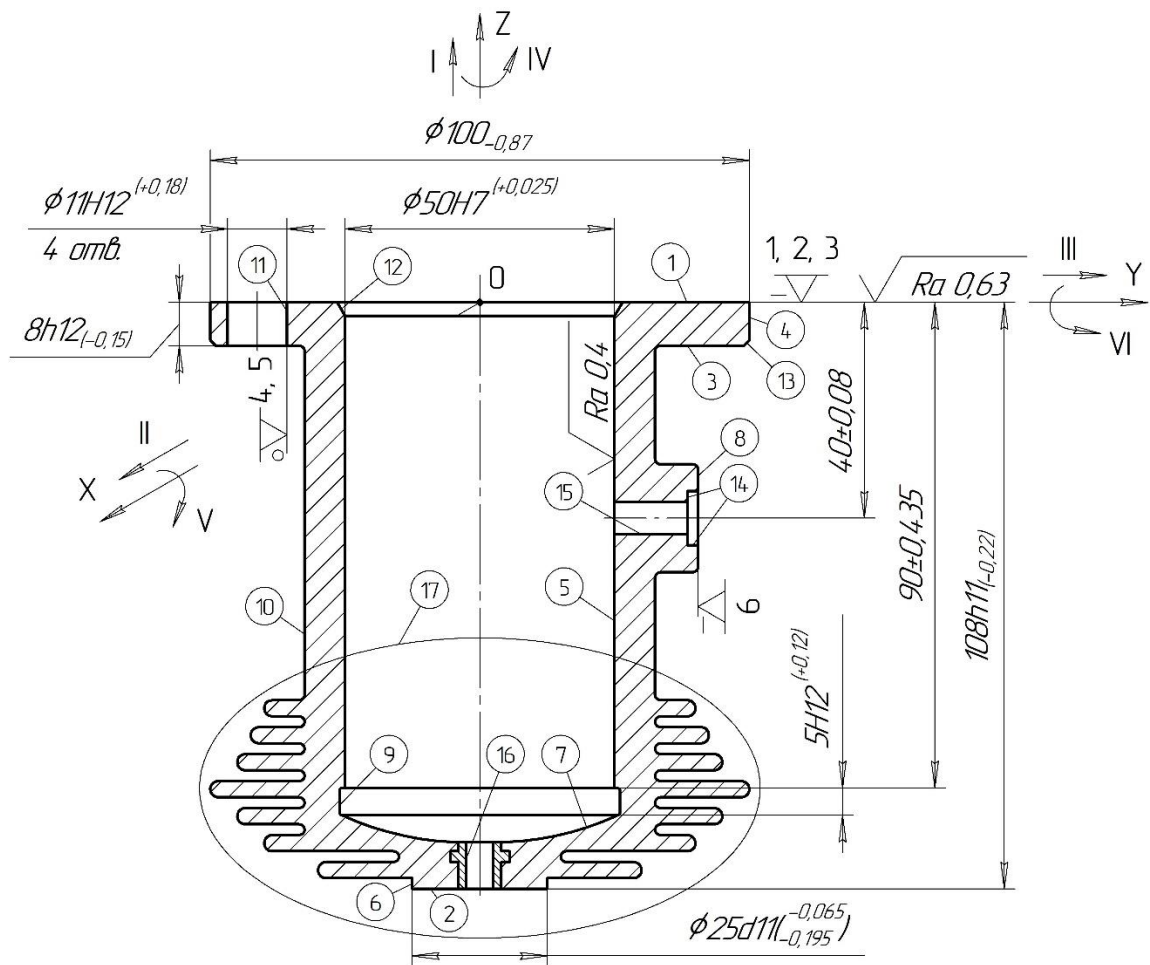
Ескіз циліндра з нумерацією поверхонь
